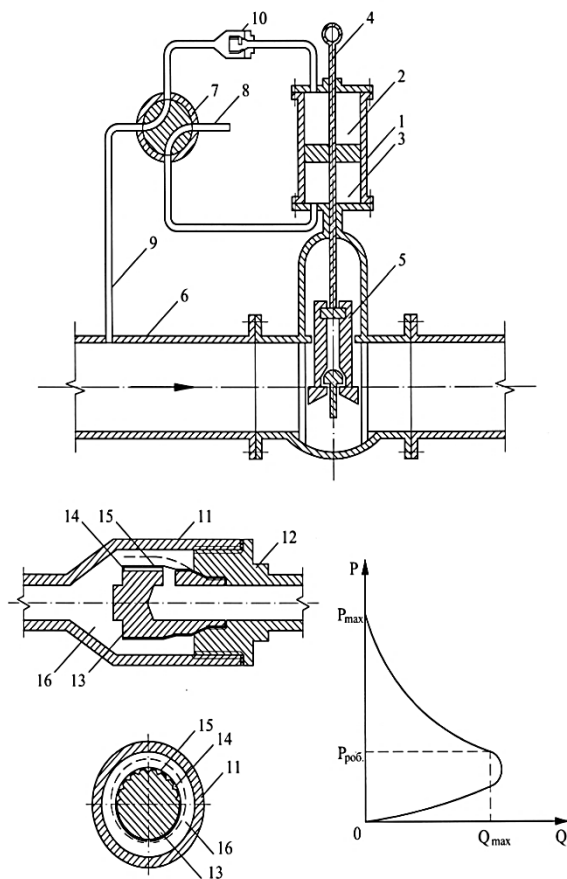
Пристрій для безударного закриття засувки: 1 – гідроциліндр; 2 – верхня камера; 3 – нижня камера; 4 – шток; 5 – засувка; 6 – напірний трубопровід; 7 – розподільчий пристрій; 8 – злив; 9 – напірна лінія; 10 – односторонній дросель; 11 – корпус; 12 – сідло; 13 – робочий орган; 14 – ряд паралельних щілин; 15 – еластична мембрана; 16 – робоча камера
